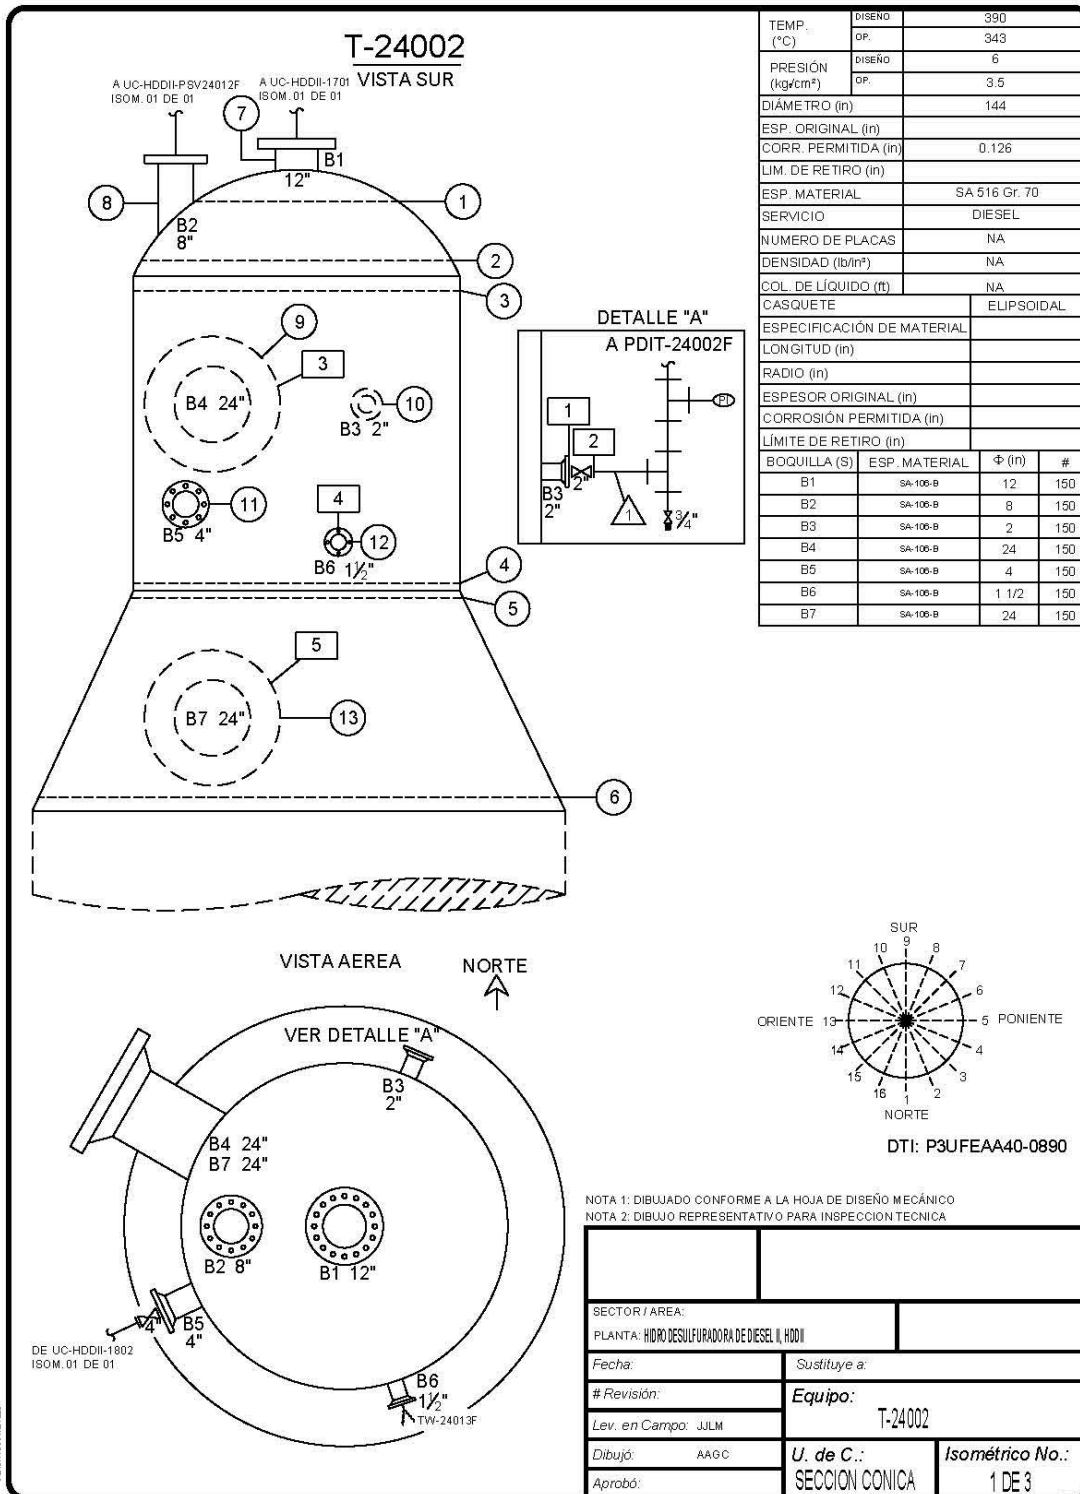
Diagrama de inspección técnica del domo del equipo en la plantilla SIMECELE.
